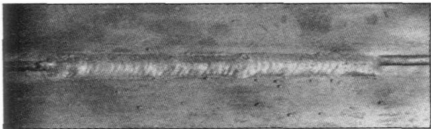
304 不锈钢水下常压 V 形坡口的堆焊焊缝
